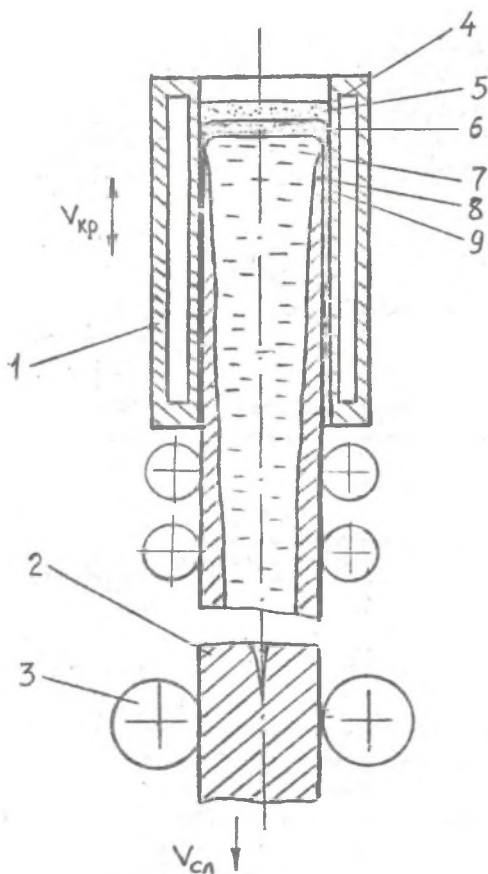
Схема непрерывного литья заготовок; 1-кристаллизатор, 2-непрерывный слиток, 3-тянущие валки, 4-водохлаждаемые рабочие стенки кристаллизатора, 5-сыпучий слой шлакообразующей смеси, 6-шлаковый расплав, 7-жидкий металл, 8-затвердевающая корка слитка, 9-смазочный слой между коркой и рабочими стенками.
